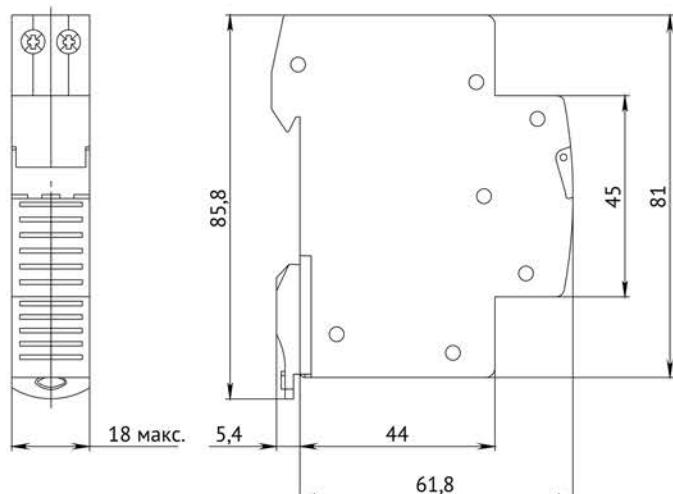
Габаритные, установочные и присоединительные размеры звонков.
